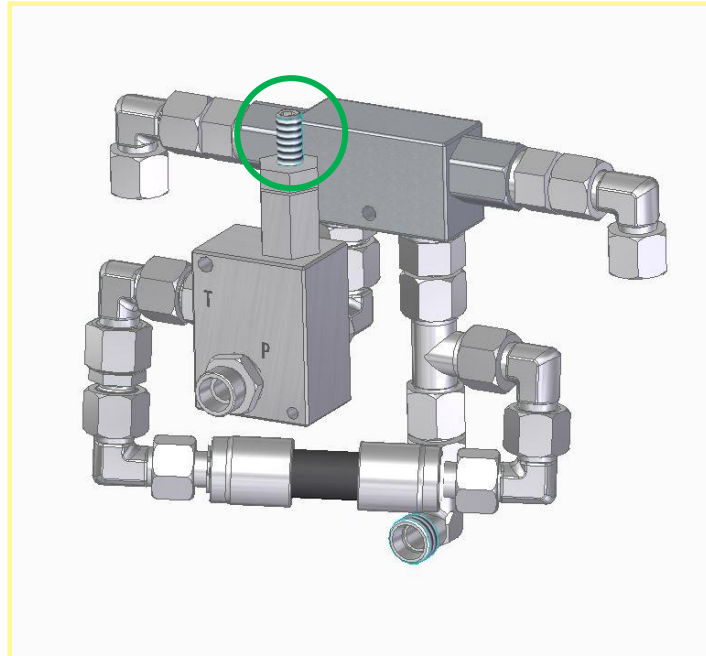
Inbusschraube – Zum Einstellen des Auslösedrucks
